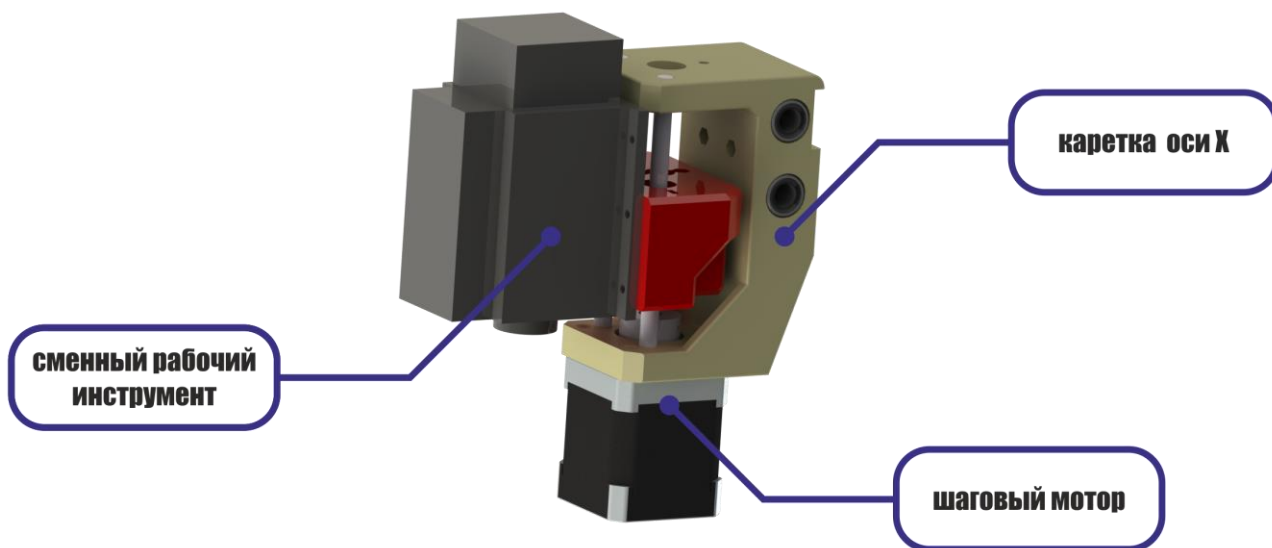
Модель каретки с установленным модулем рабочего инструмента (лазер)
